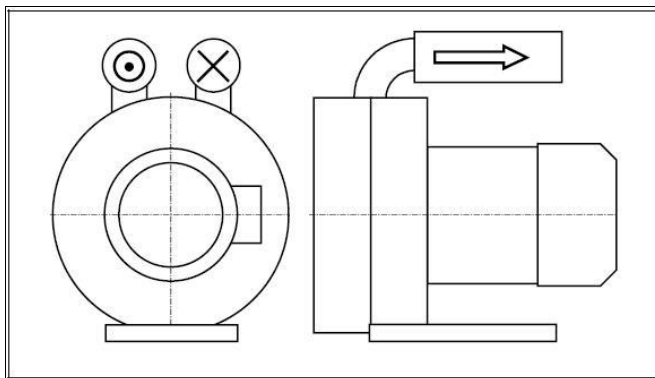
Двухпоточная конструкция вакуумного насоса/компрессора с двумя рабочими колесами.
